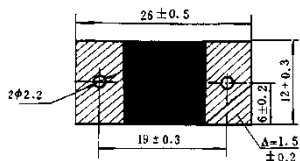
MSC04 型湿敏电阻器外形尺寸图
